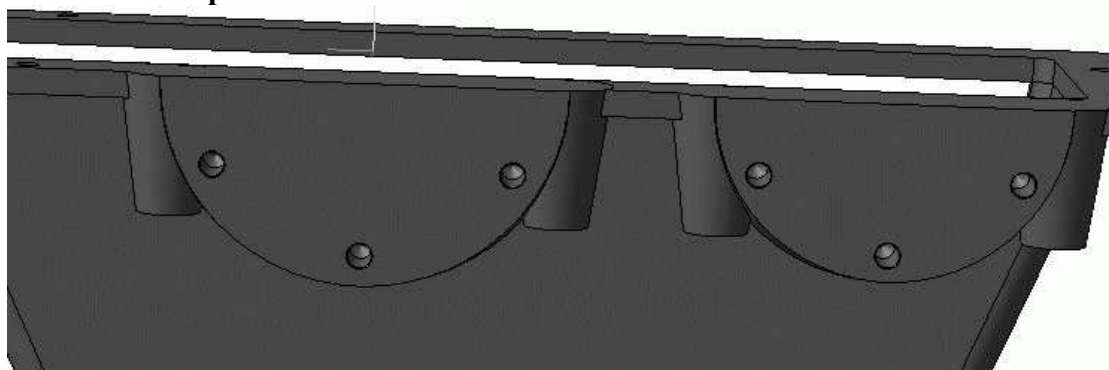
Отверстия под фиксирующие винты в местах крепления крышек подшипников
